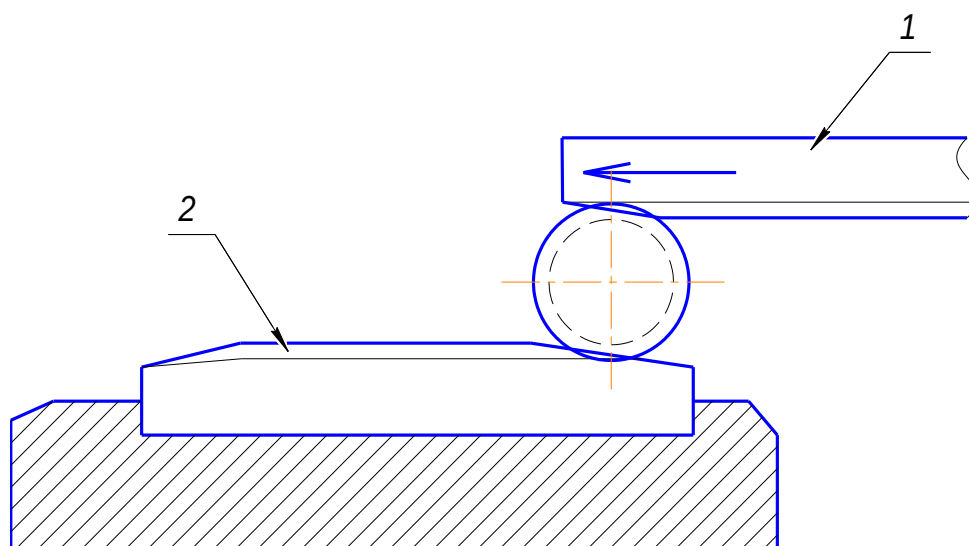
Накатывание двумя плашками: 1 – подвижная плашка, 2 – неподвижная плашка
